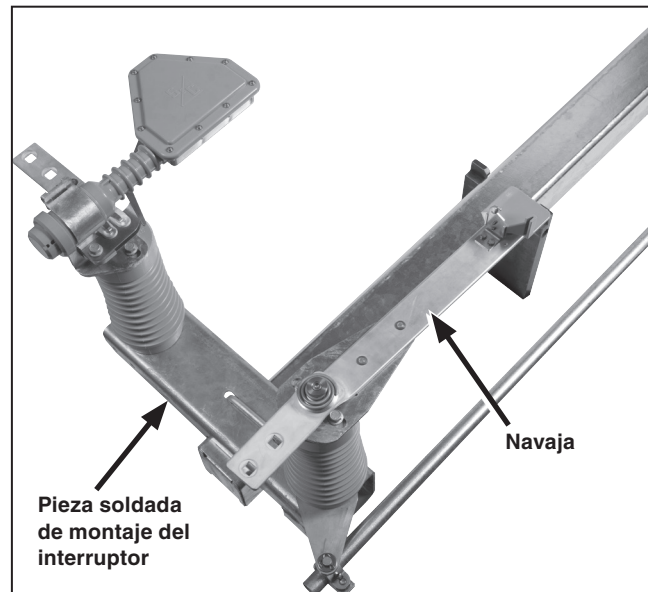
La navaja en 90 grados desde la posición de la pieza soldada del montaje.
